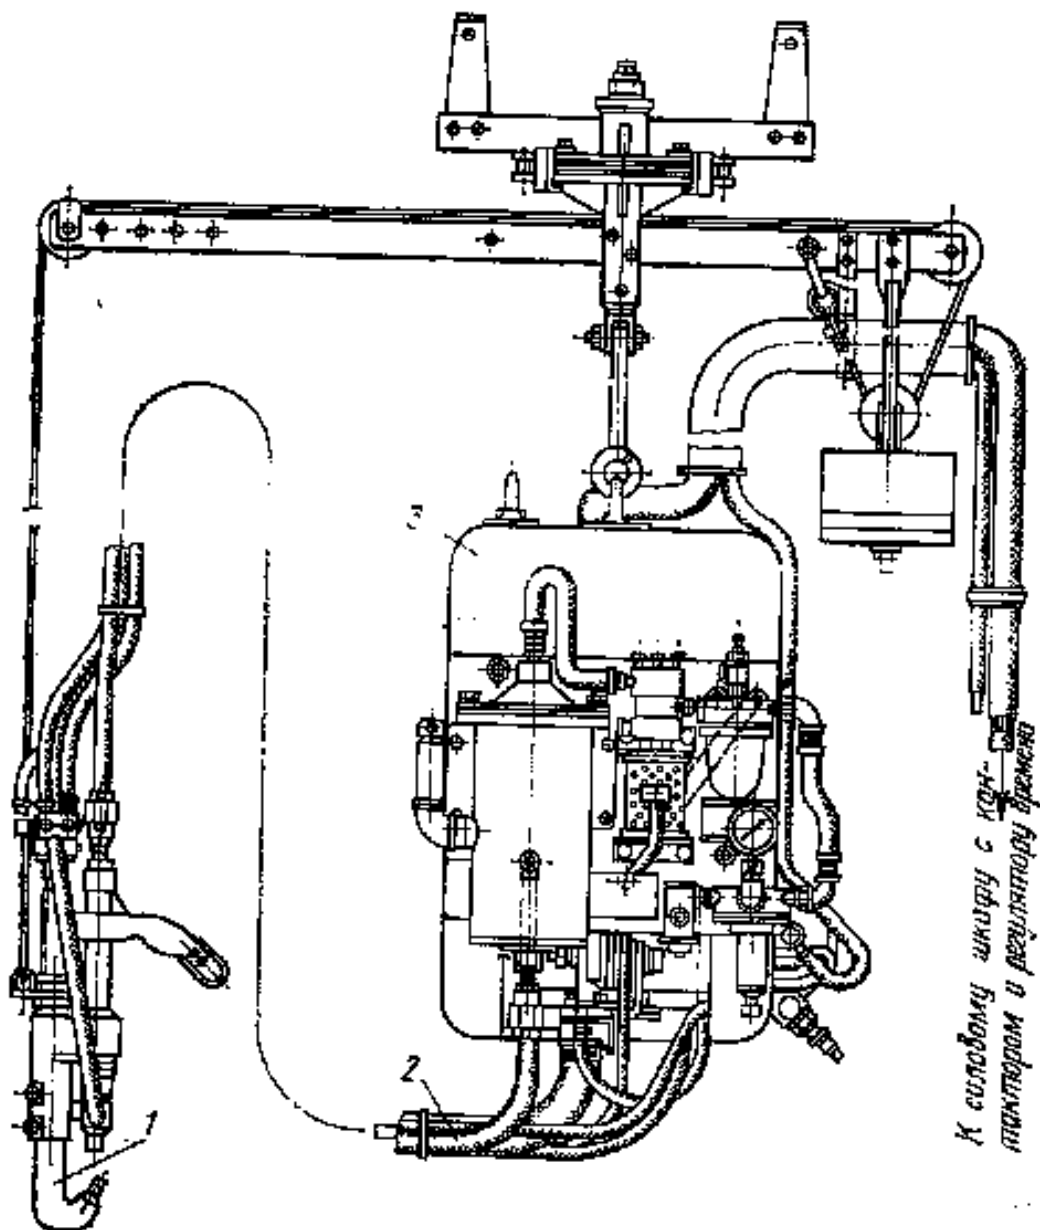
Подвесная сварочная машина МТП-806
